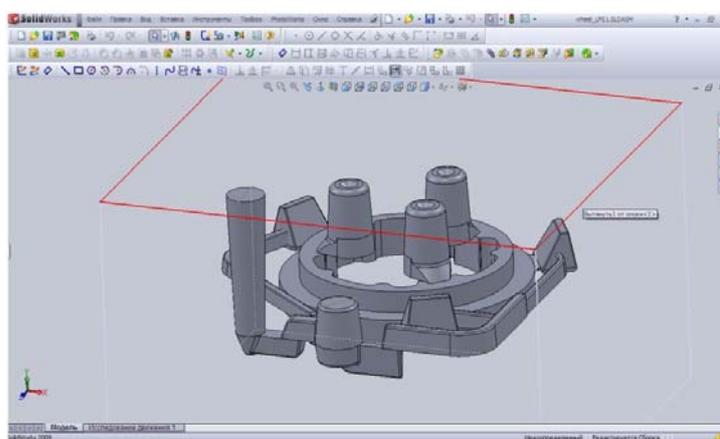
Трёхмерная модель отливки «Колесо»
